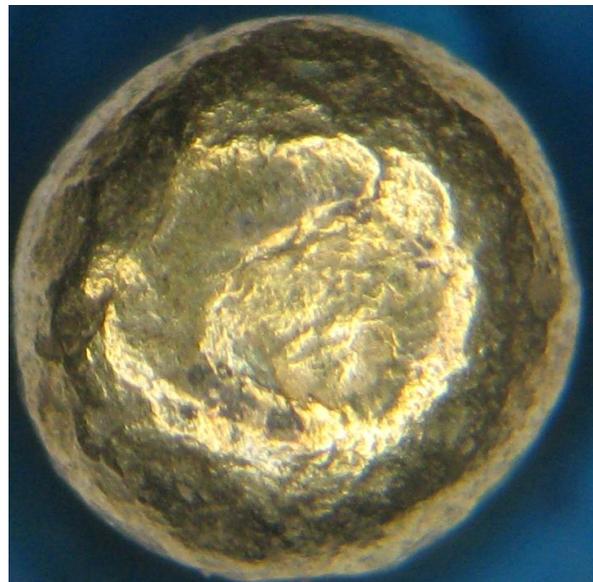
След на вершине одного из штифтов корпуса в месте его контакта со штифтом цилиндра
